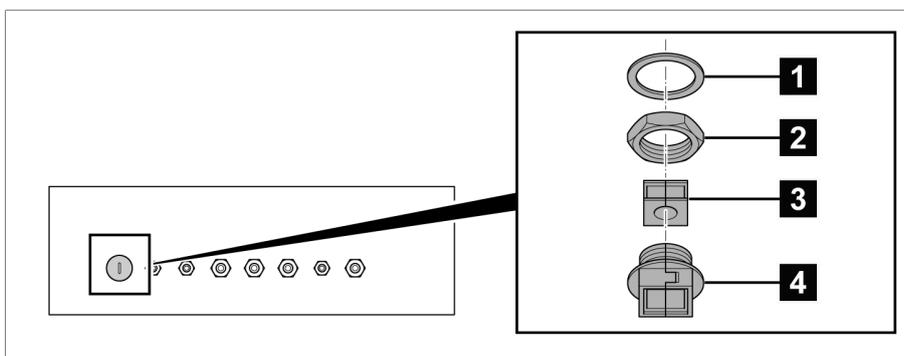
Kabeldurchführung für Verbindungsleitung zum Motorantrieb
